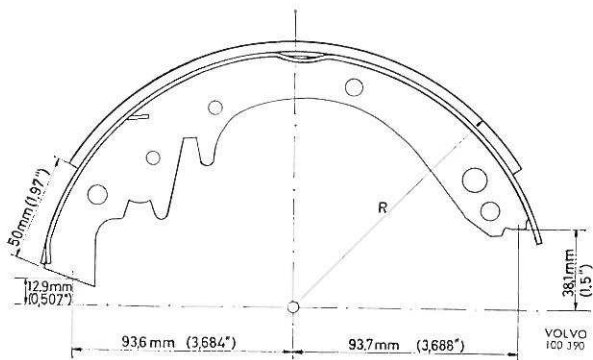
Cote de réglage pour segments arrière des roues arrière.
